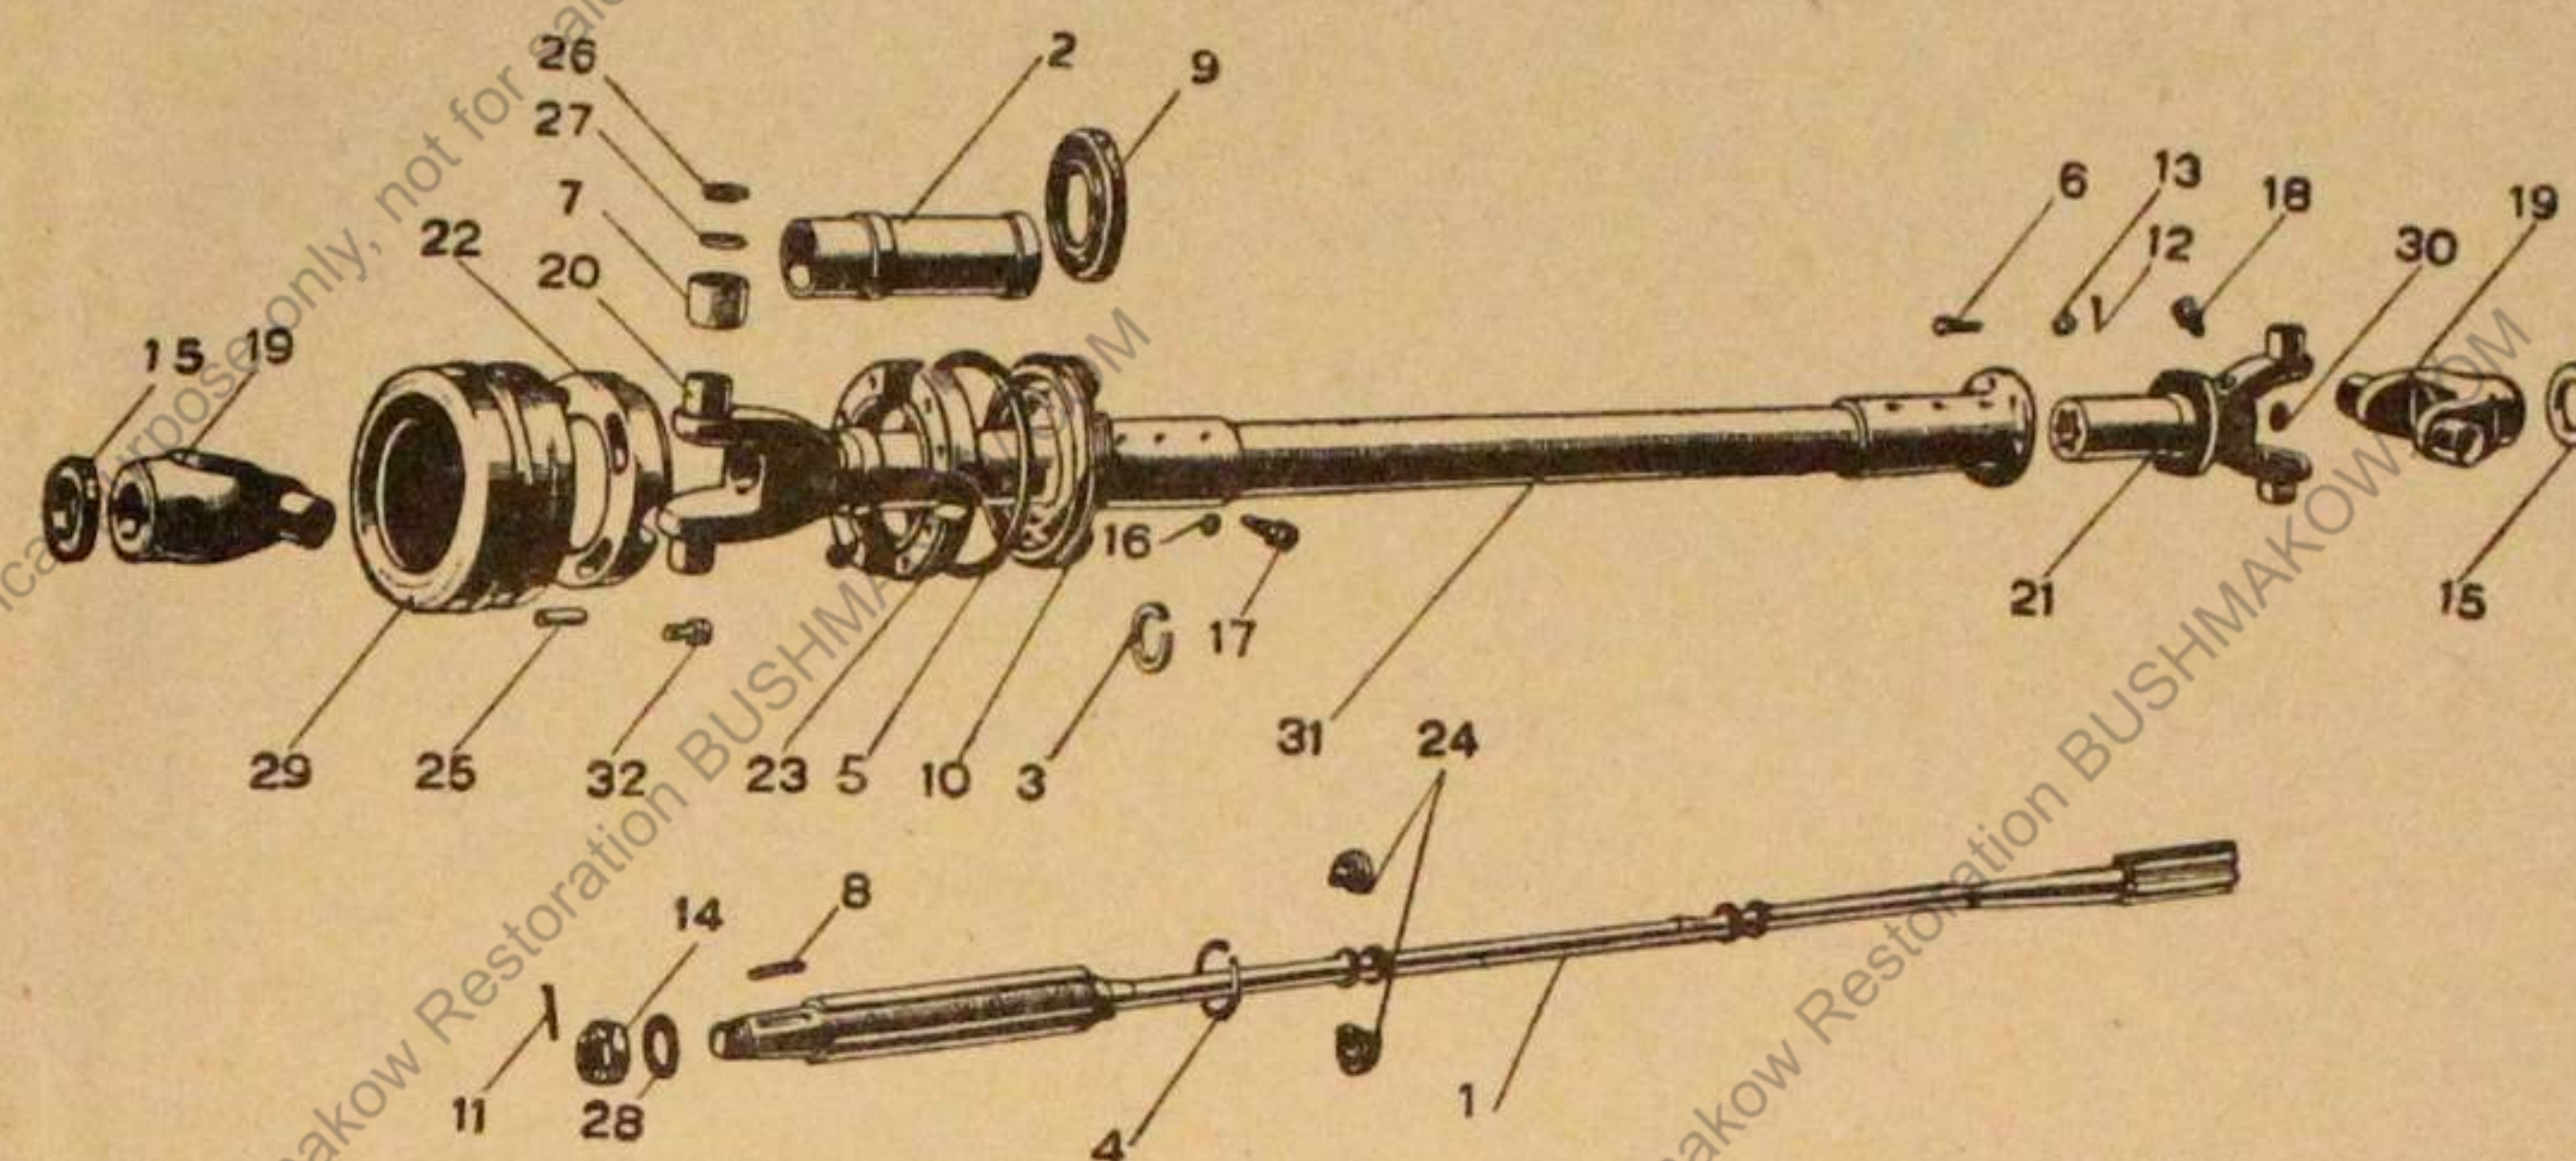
Gelenkwelle für Serie PC 26 und PC 30
